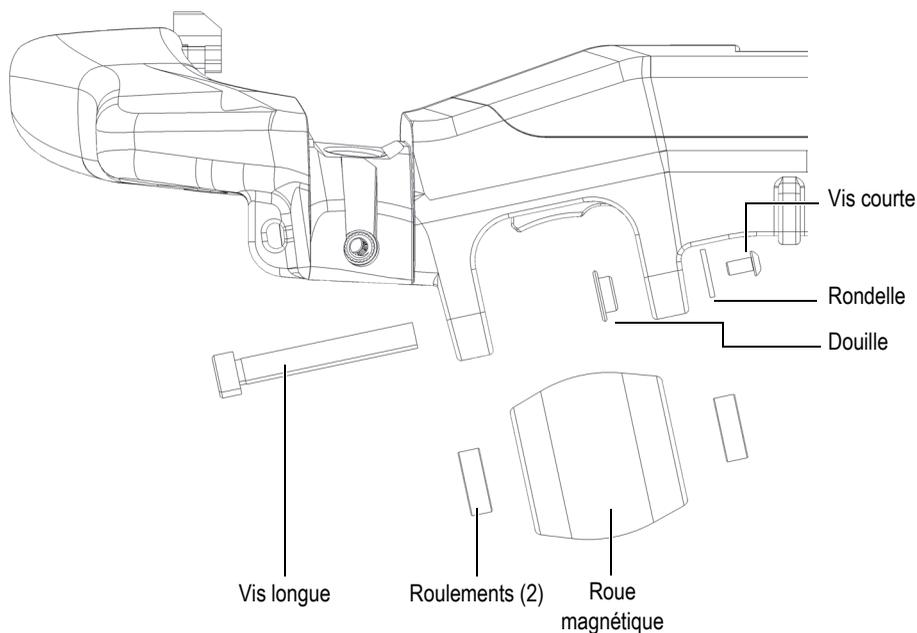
Démontage et remplacement d'une roue magnétique — Pièces
